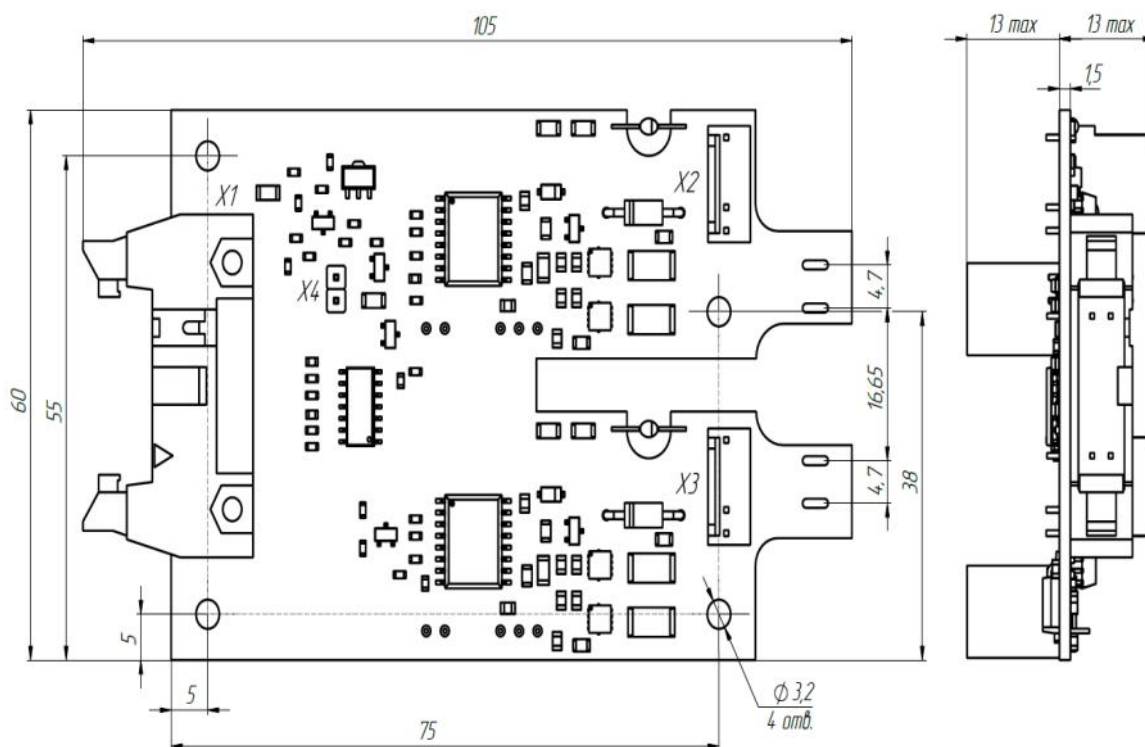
Чертеж драйвера DI28-17-E-2
